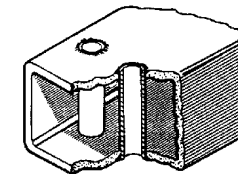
Taladrar el perfil y soldar a éste un tubo distanciador de guía
